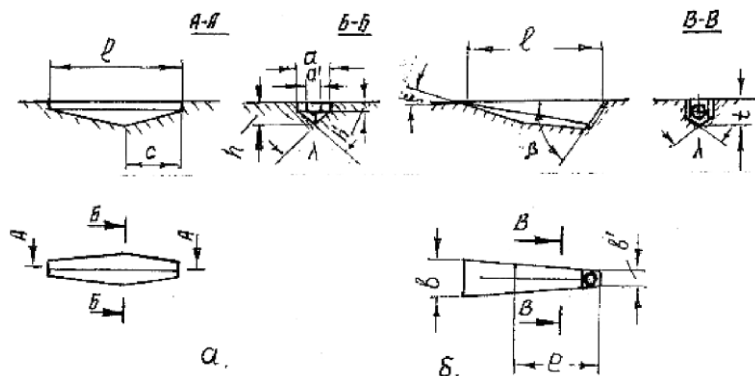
Продолговатая «мелкая» ячейка овсюжного цилиндра конструкции Козлова Д.А.
